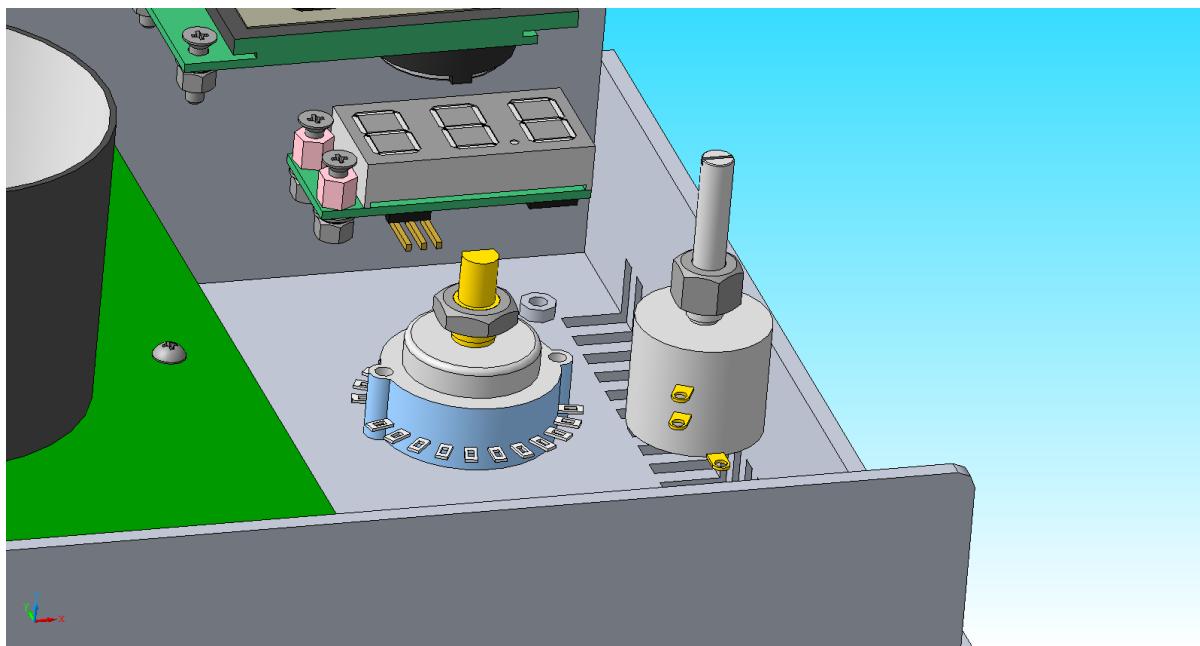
Расположение в корпусе потенциометра и переключателя (крышка корпуса не показана).
